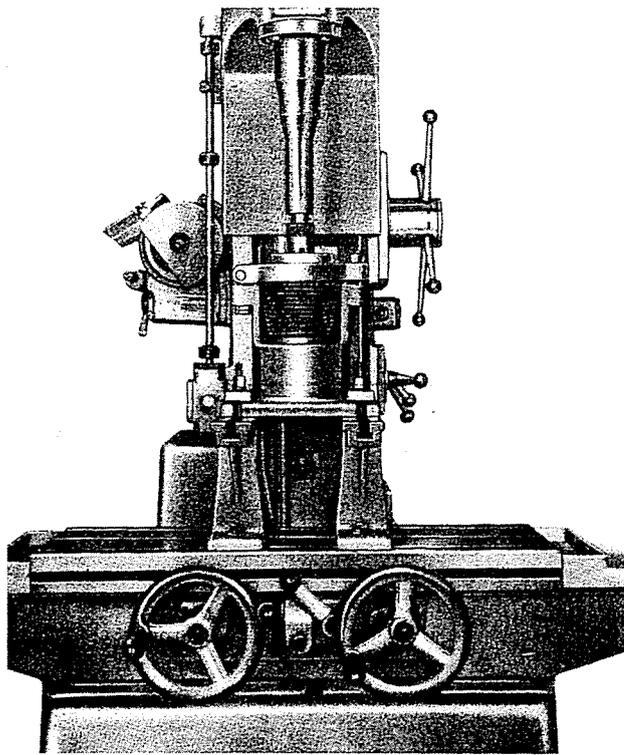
Ausbohren eines mit dem Werkzeug A. 60000 auf der ortsfesten Maschine aufgespannten Zylinders.
